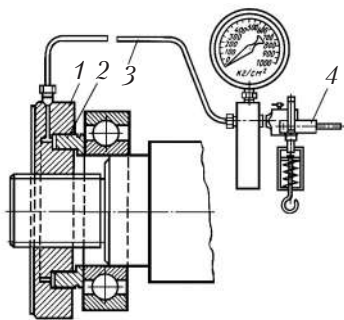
Пристосування для запресування великогабаритних підшипників:
